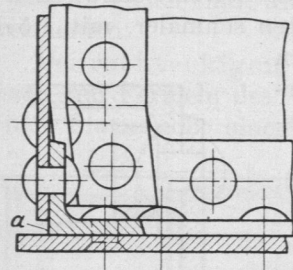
Eckverbindung unter Verschweißung des Winkeleisens am Boden.
